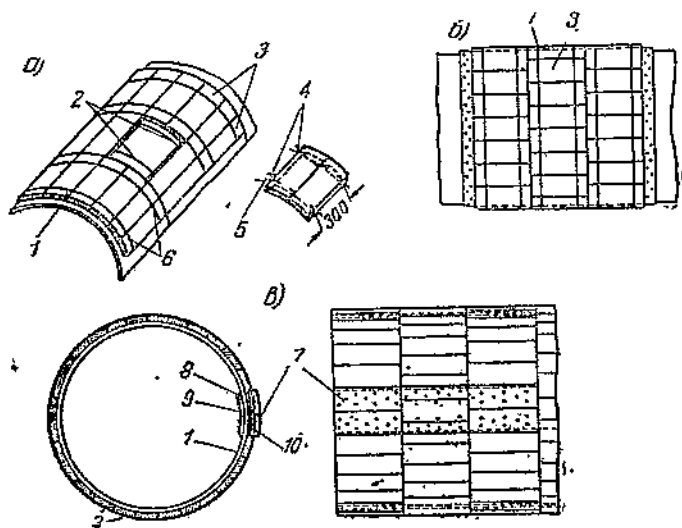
Изоляция цилиндрической части паровозного котла: а — укладка и крепление плит петлями на цилиндрической части котла; б — укладка плит на цилиндрической части котла; в — изоляция продольного заклепочного шва на цилиндрической части котла
